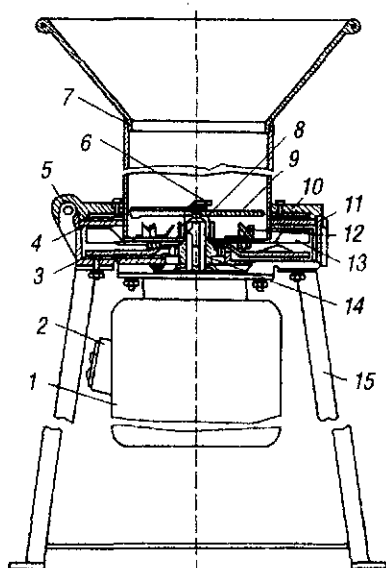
Схема корнерезки КПИ-4: 1 – электродвигатель; 2 – магнитный пускатель; 3 – выбрасыватель; 4 – дека; 5 – палец шарнира; 6 – специальный болт; 7 – бункер; 8 – ступица верхнего диска; 9 – верхний диск с ножом; 10 – крышка камеры измельчения; 11 – корпус камеры измельчения; 12 – вертикальные ножи; 13 – лопасти нижнего диска; 14 – ступица выбрасывателя; 15 – станина
